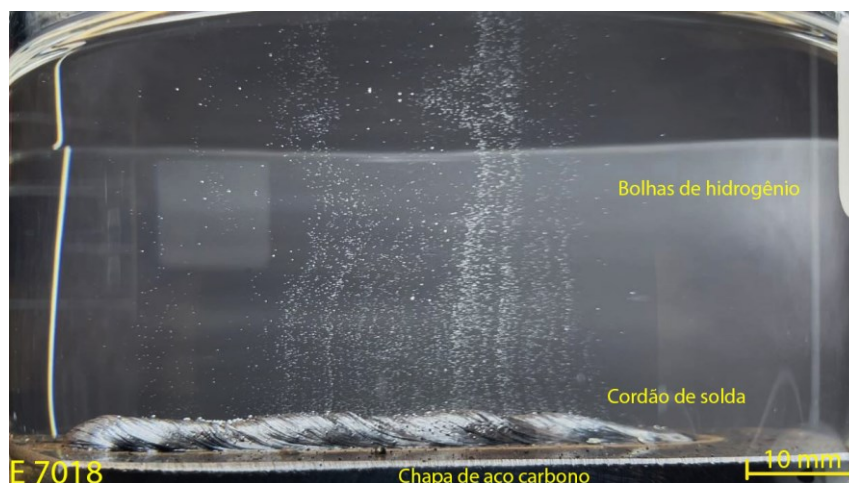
Experimento de difusão de hidrogênio em óleo mineral em cordão de solda depositado com o processo SMAW usando eletrodo básico 7018 [<https://youtu.be/U3Ymn0z9HNU>].
